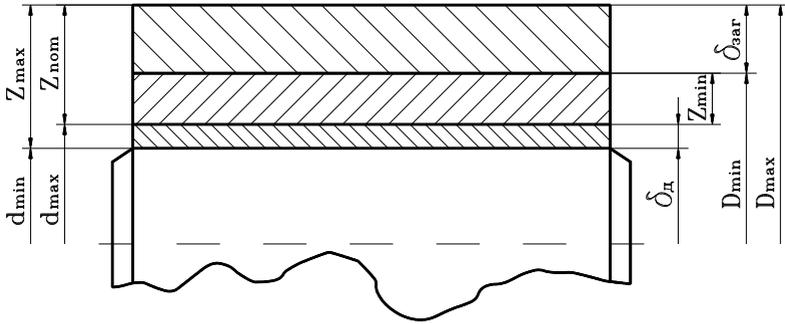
Пример расположения полей припусков и допусков при индивидуальной настройке станка на размер
